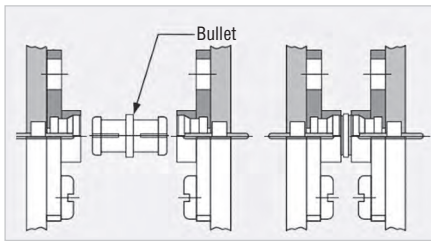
Соединение печатных плат с помощью адаптера «bullet» и двух соединителей SMPM вилка
